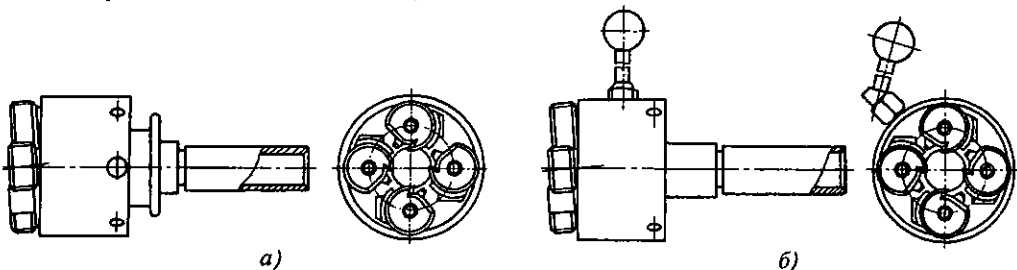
Винторезные самооткрывающиеся головки с круглыми гребенками
